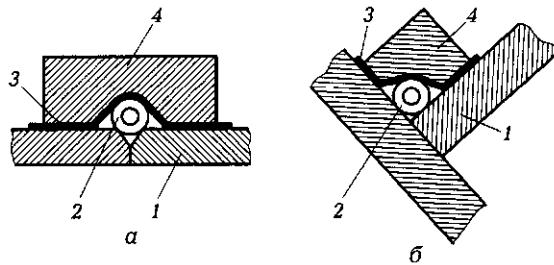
Схемы сварки лежачим электродом стыкового [а] и таврового [б] соединений:
